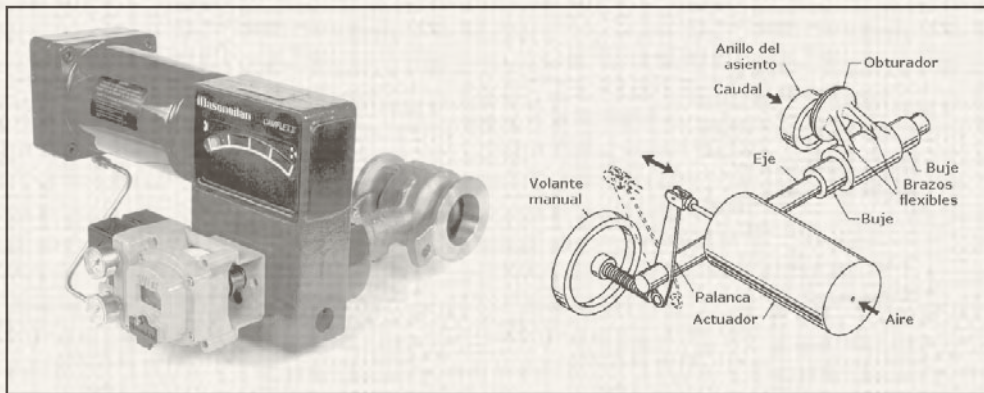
Válvula Camflex. Fuente: Masoneilan (Dresser)
